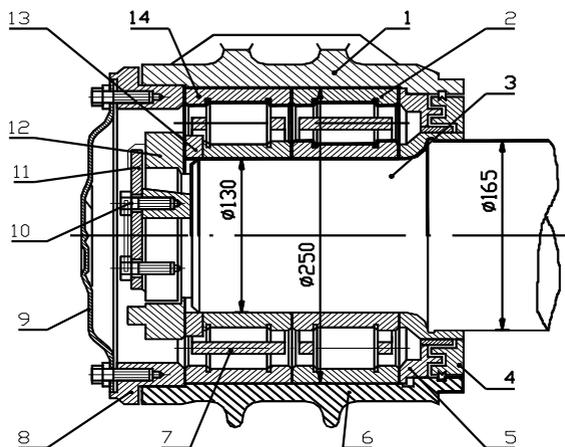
Букса с роликовыми цилиндрическими подшипниками:
